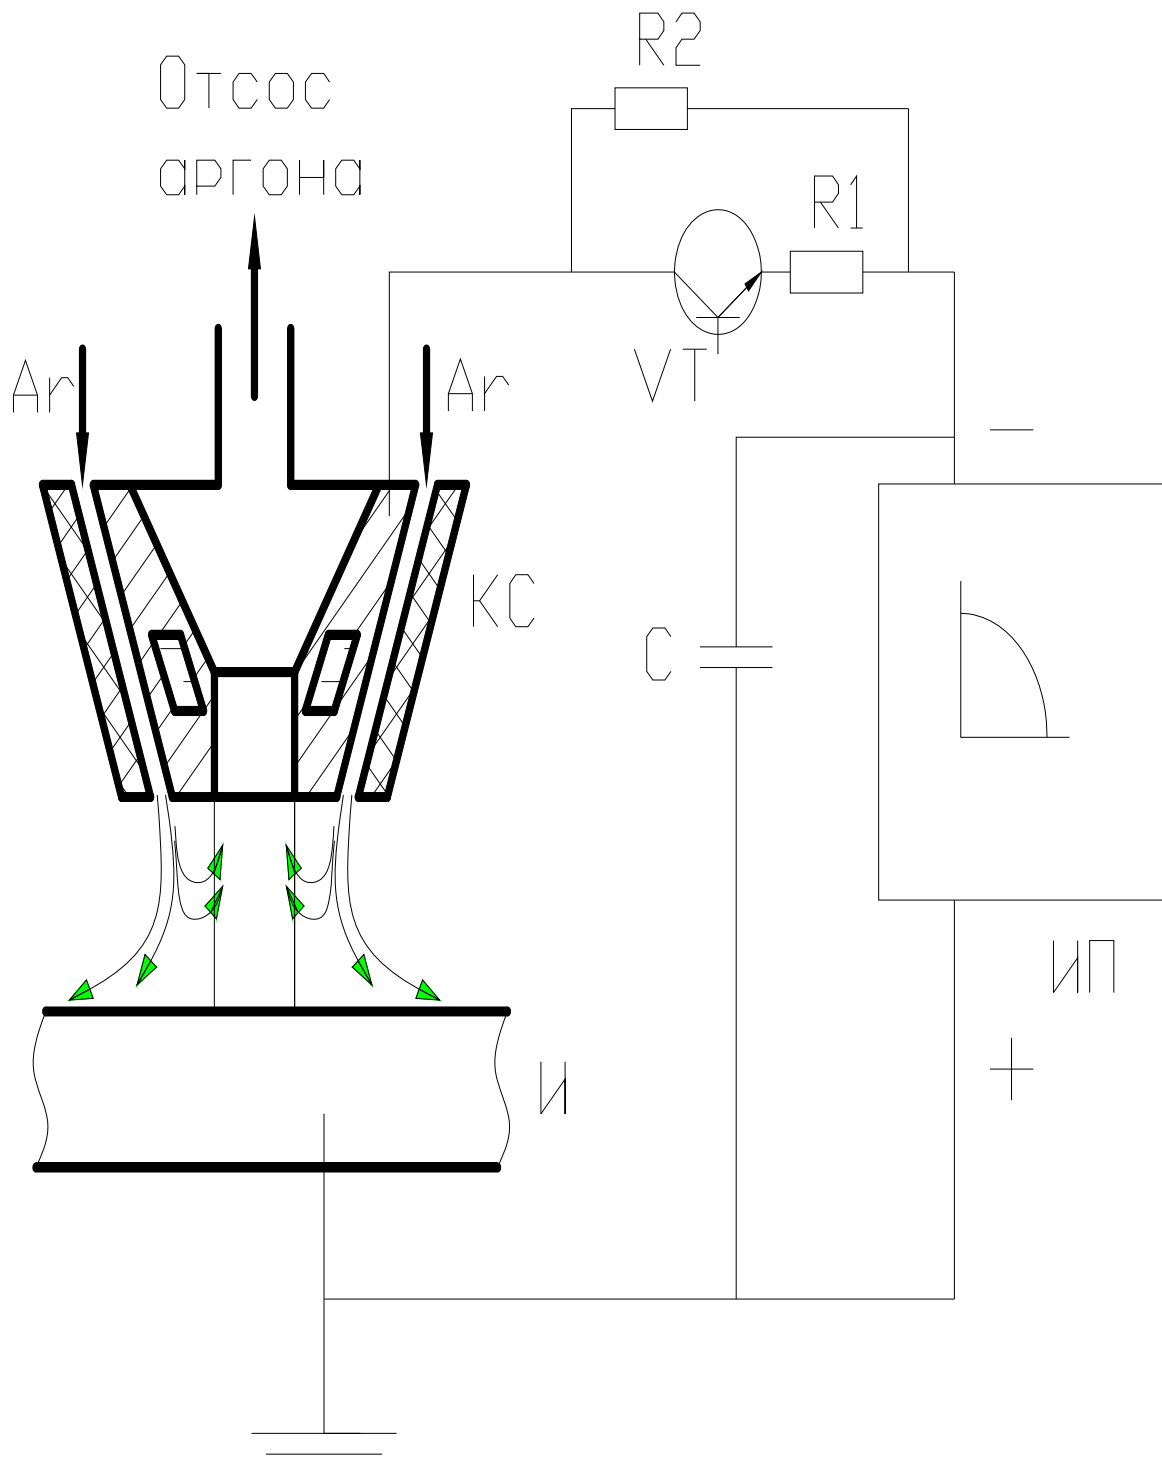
Схема установки для плазменной наплавки с обратным потоком плазмообразующего газа:
